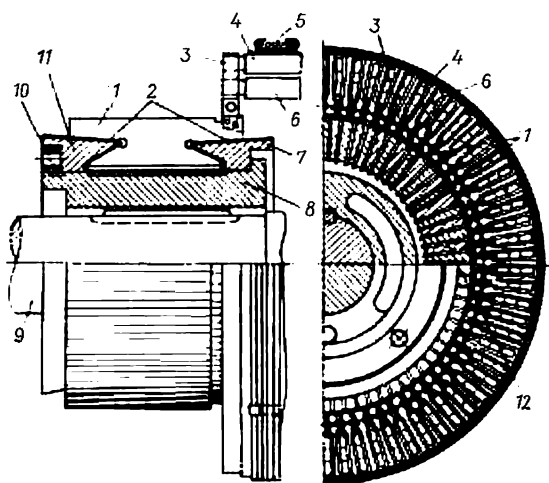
Raccordement des sections de l'enroulement d'induit au collecteur.
